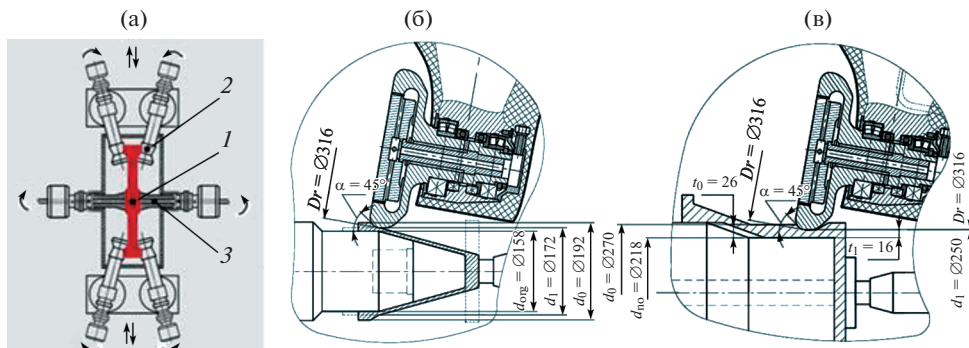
Принципиальная схема процесса раскатки в условиях сверхпластичности заготовок: (а) — диска; (б) — цилиндрической и конической частей полого вала из листовой заготовки; (в) — цилиндрической части полого вала из штампованной заготовки.
